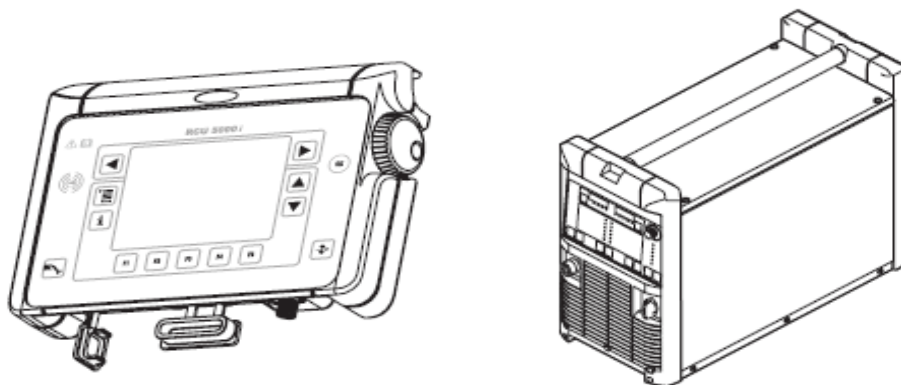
Equipos de control y potencias de un sistema de soldadura al arco FRONIUS
